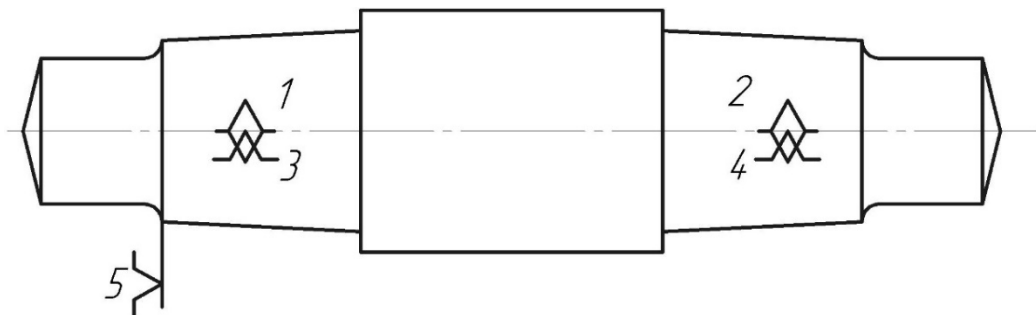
Теоретична схема базування заготовки вала для першої операції
